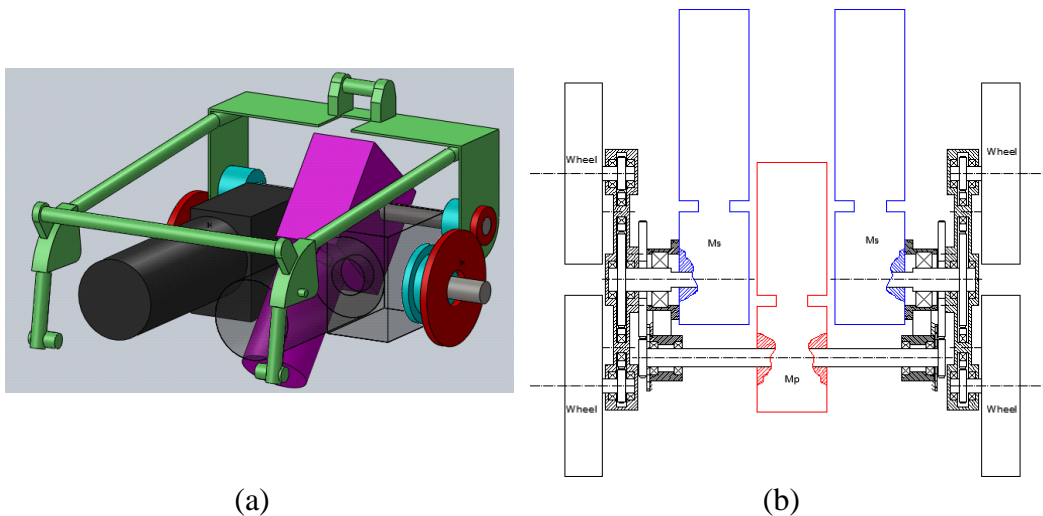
Sistema di attuazione della carrozzina montascale: (a) vista assonometrica; (b) vista dall'alto [42], [43]
